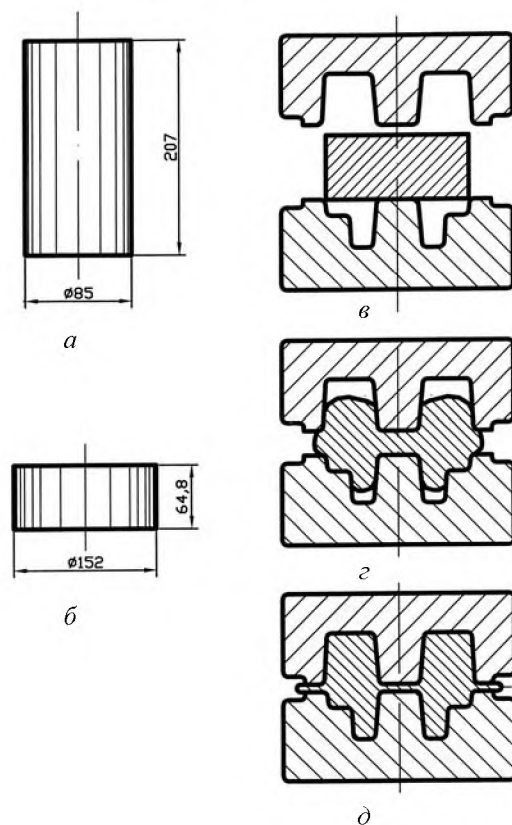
Этапы изготовления поковки на прессе штамповкой в торец:
